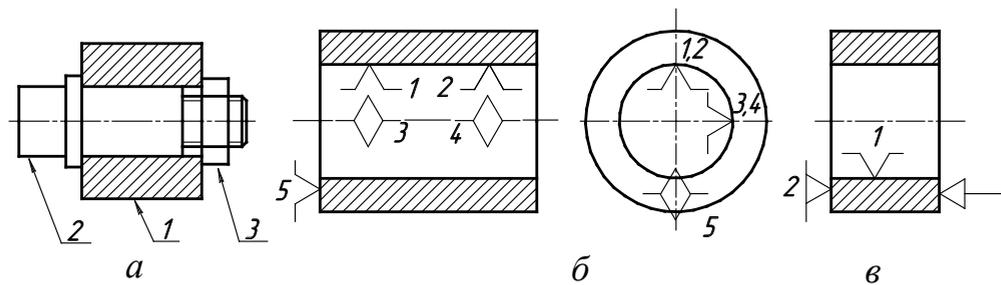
Установка длинной втулки на цилиндрической оправке:
